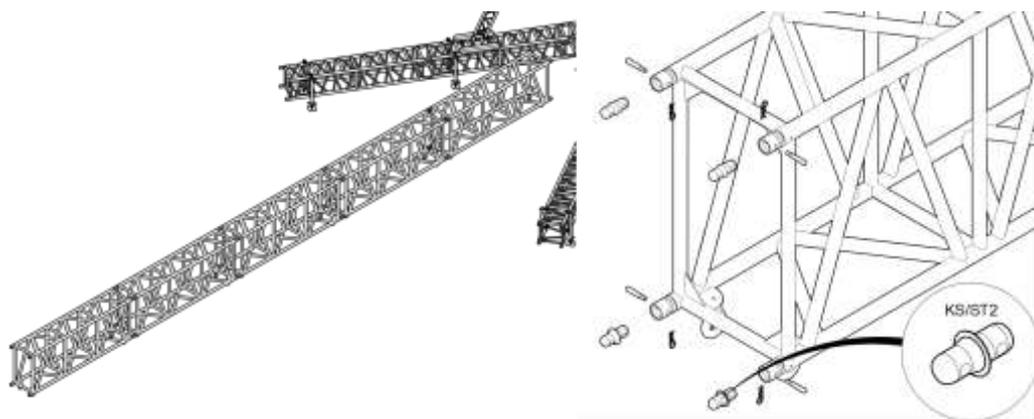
Montaggio struttura di sollevamento torre – braccio posteriore; regolazione slitta.
